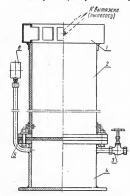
Камера вихревого наплавления: 1 — конух отсоса; 2 — корпус камеры; 3 — вентиль для подвода газа; 4 — опорная часть камеры; 5 — пористое дно (минора); 6 — манометр.
